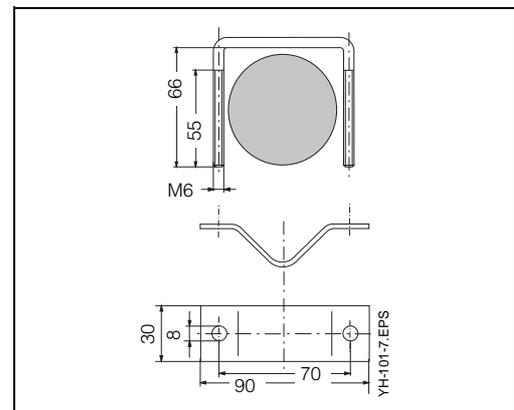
Rundmastbefestigung für Wetterschutzdach CYY 101, wenn nicht an Armaturenhalterung CYH 101 montiert wird
